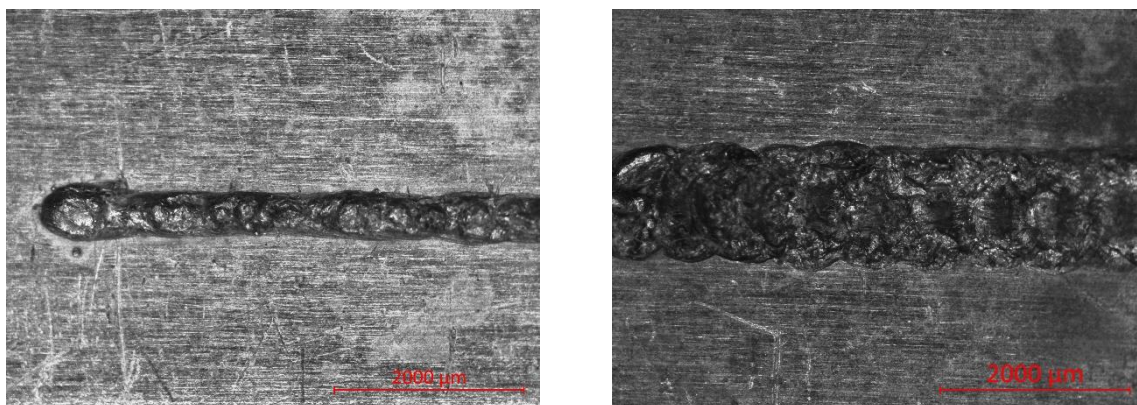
Esempi di immagini macroscopiche: a sinistra saldatura lineare, a destra saldatura con tecnica wobbling
